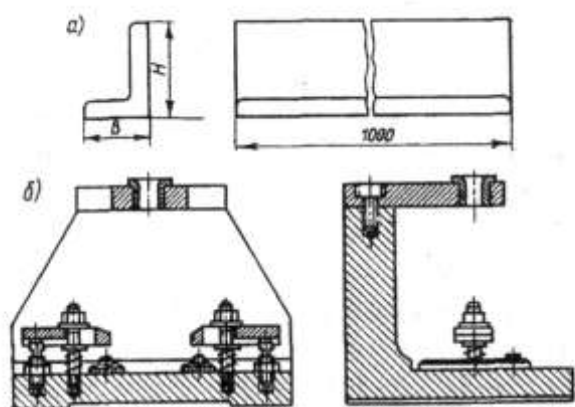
Заготовка корпуса приспособления из неравнобокого угольника (а) и расположение его в приспособлении (б)
